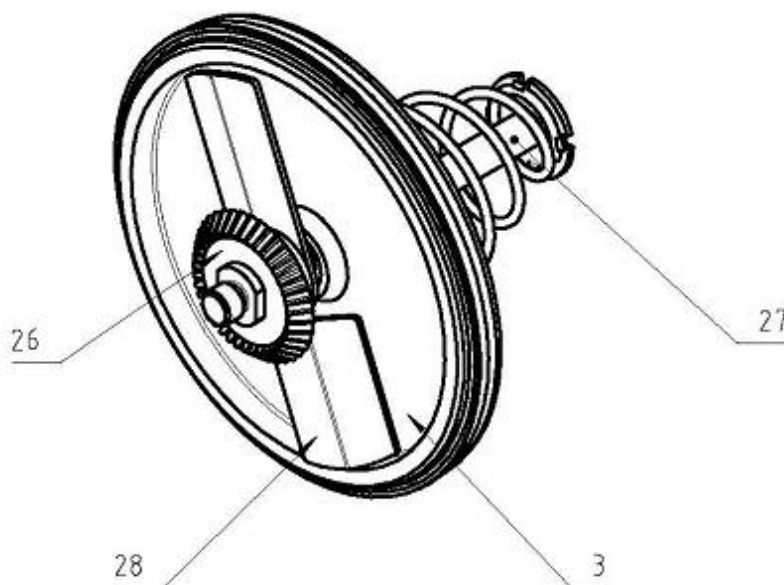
(Направляющий стержень, шайбовый поршень и разводящая лопатка)
